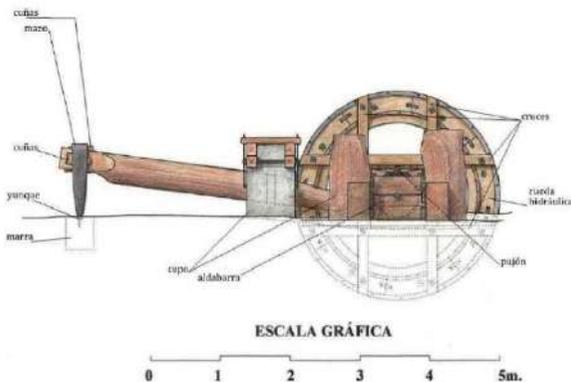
Configuración de un martinete, vista en alzado. Fuente: Soler (2006).
